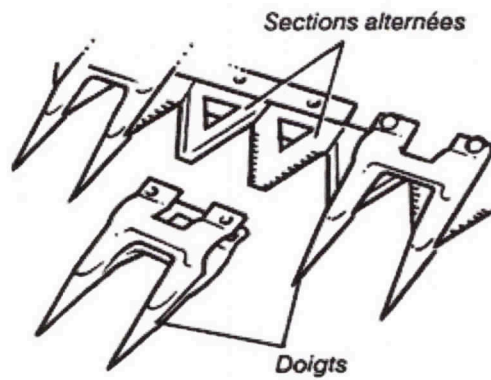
Vue partielle d'une barre de coupe à section alternées
